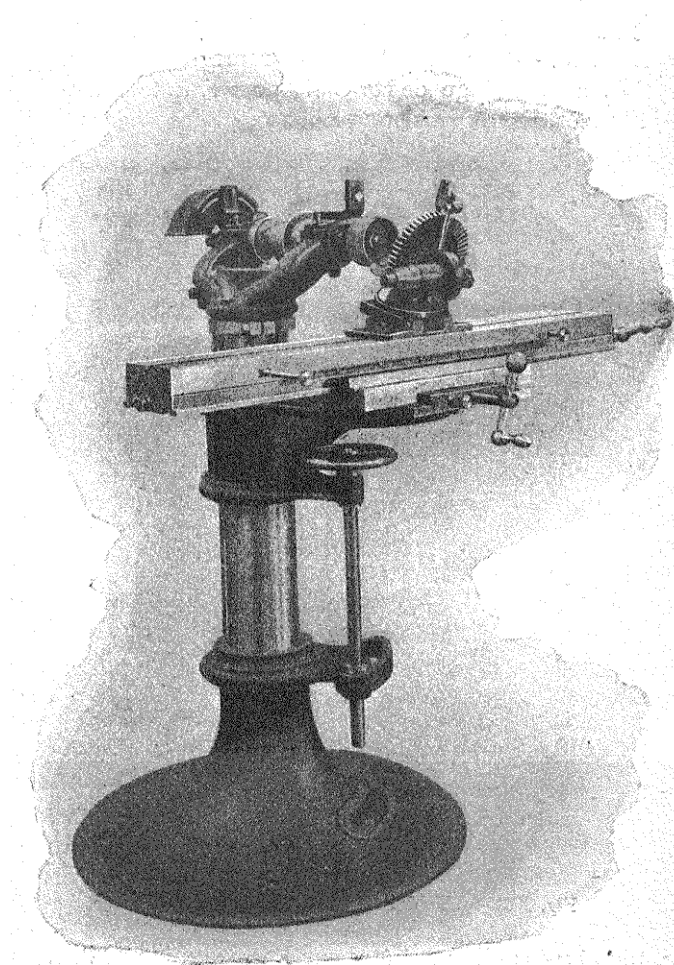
Machine universelle à affûter les outils Reinecker.
